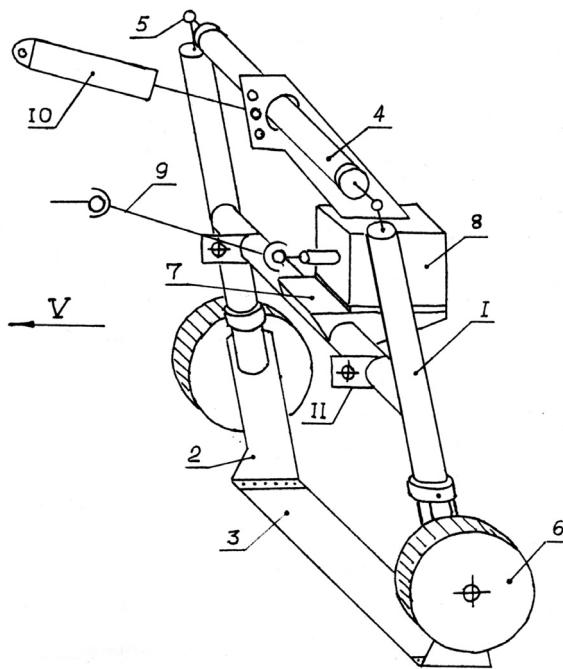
Подрезчик корней горизонтальный для лесных питомников: 1 – рама; 2 – черенок; 3 – нож; 4 – стяжка; 5 – шарнир; 6 – опорное колесо; 7 – плита; 8 – вибратор; 9 – соединительный вал; 10 – регулятор угла резания; 11 – кронштейн навески
